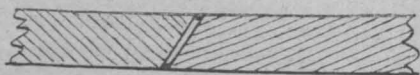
Mangelhaft ausgeführte Schweißung.
